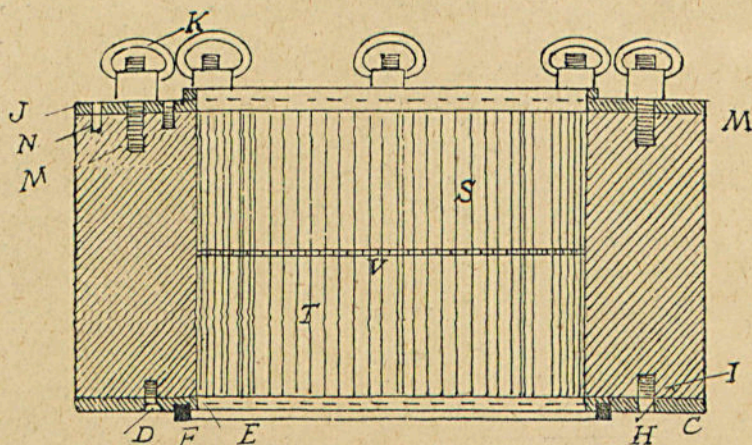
Turbine Adant. Vue du panier en coupe.
